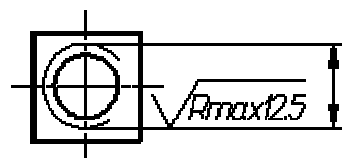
Пример обозначения шероховатости внутренней резьбы
